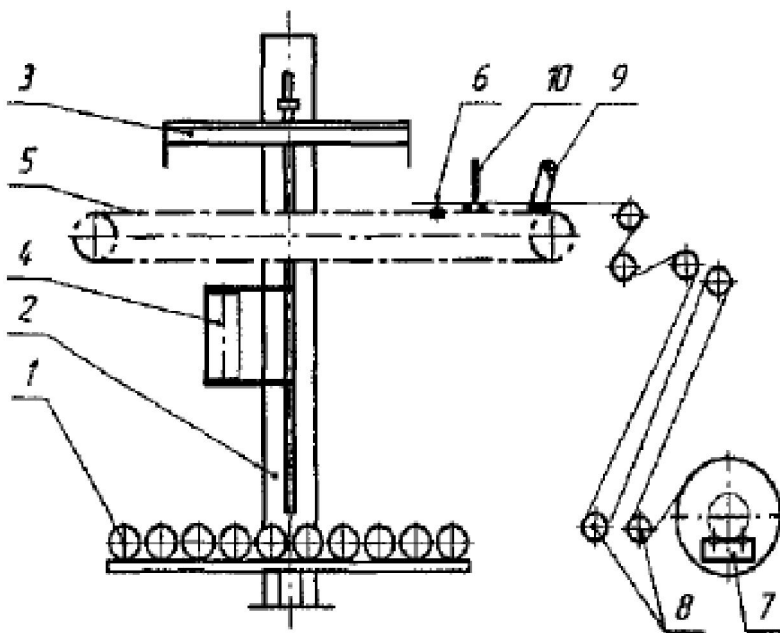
Пристрій для обгортання пакет-піддону плівкою
